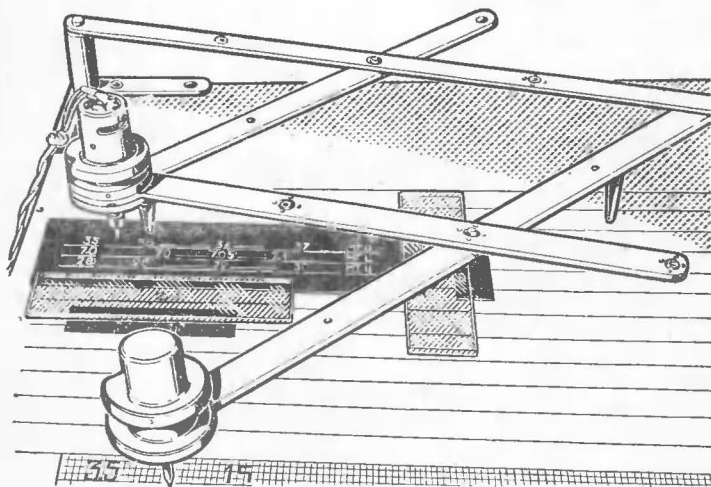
Конструкция подвижного шарнира двигателя с двигателем и фрезой
